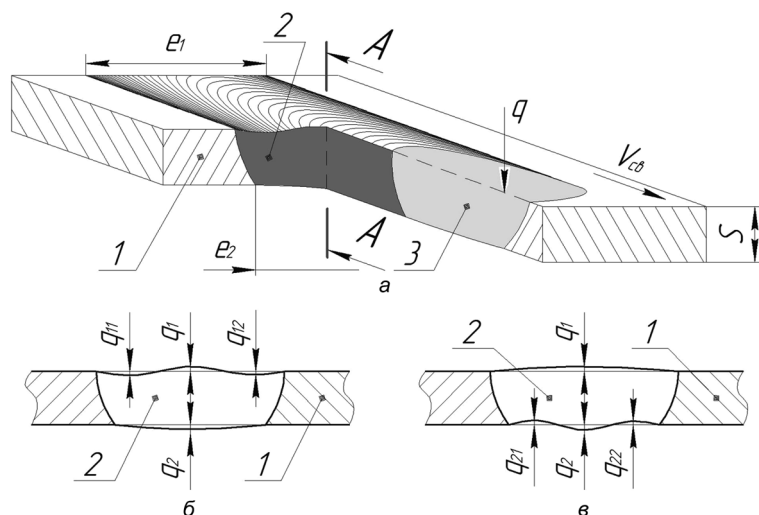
Схемы сварных соединений листового материала, получаемых с помощью ЭЛС: а – общий вид; б, в – вид А-А (поперечное сечение сварного шва); 1 – основной металл; 2 – металл сварного шва; 3 – жидкая сварочная ванна
